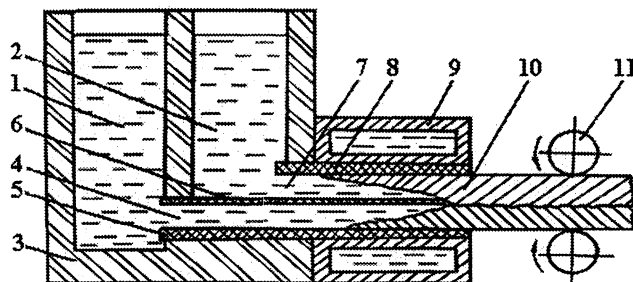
Схема установки горизонтального типа для получения биметаллических прямоугольных заготовок: 1 – металл 1; 2 – металл 2; 3 – металлоприемник; 4 – нижний канал; 5 – нижняя графитовая вставка; 6 – пластина; 7 – верхний канал; 8 – верхняя графитовая вставка; 9 – водоохлаждаемый корпус кристаллизатора; 10 – биметаллическая отливка; 11 – тянущие клети.
